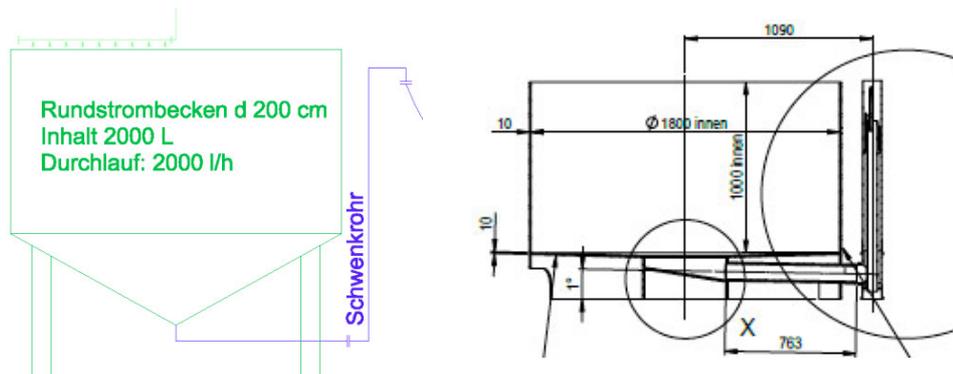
Bassins tels que proposés par M. Gallusser (à gauche) et bassins installés à Estavayer (à droite) [9, 10]
